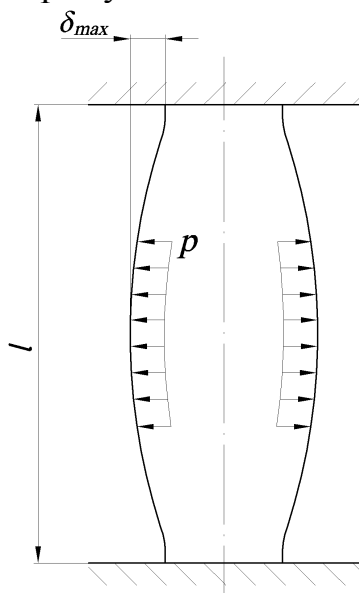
Розрахункова схема для визначення прогину шліцевого вала при обробленні напівкруглих канавок
